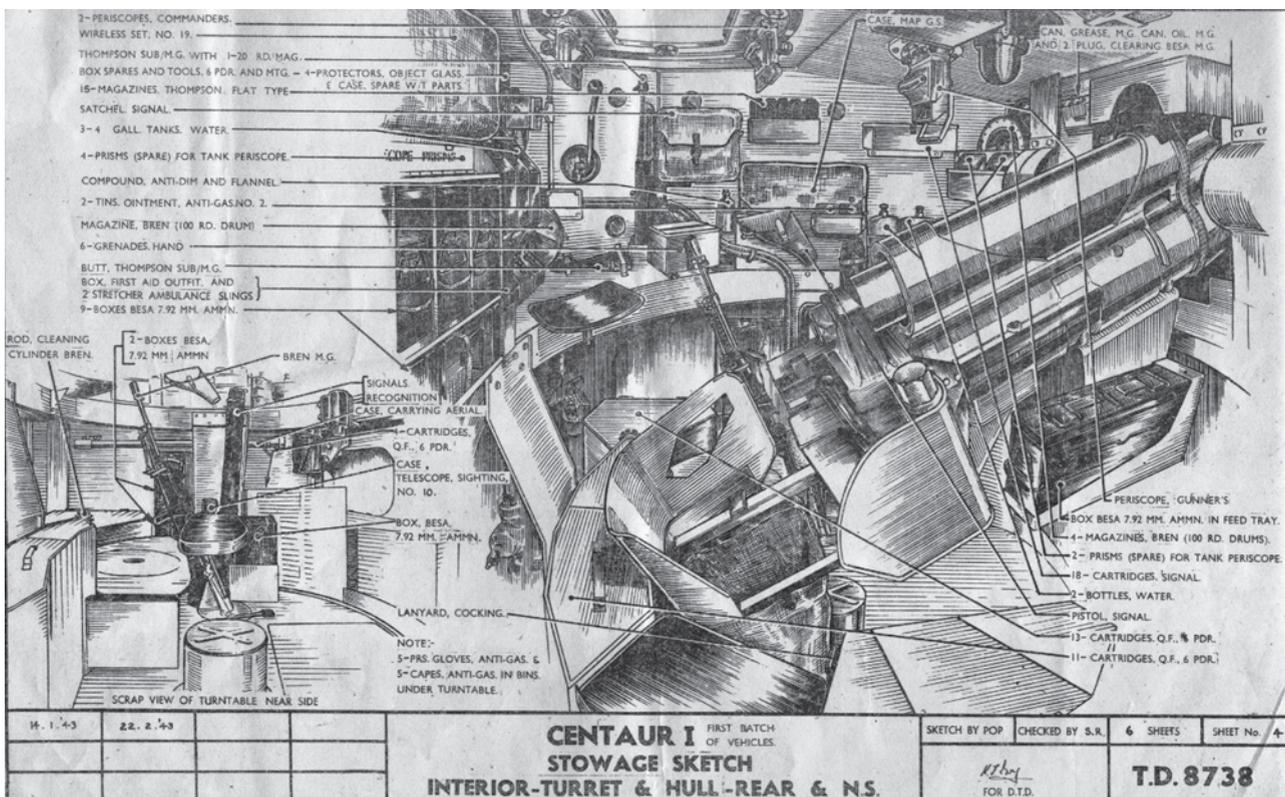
Plano de carregamento (interior da torre) do CC Centauro.
